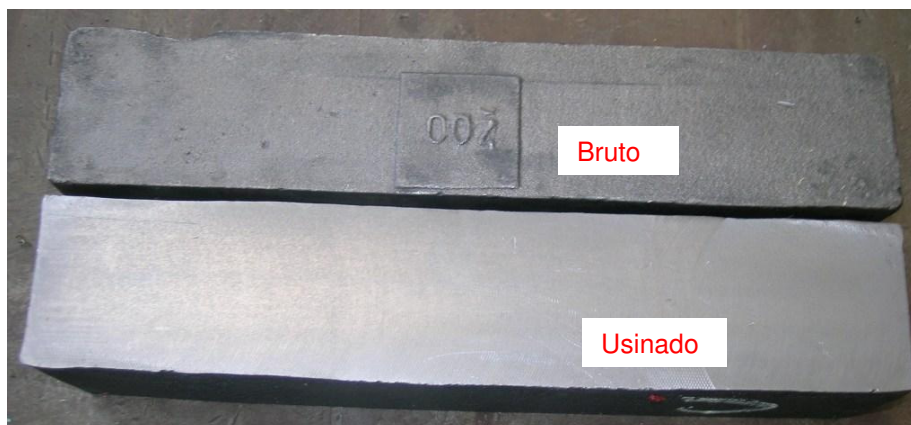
Face inferior do corpo-de-prova usinada e em bruto de fundição.
